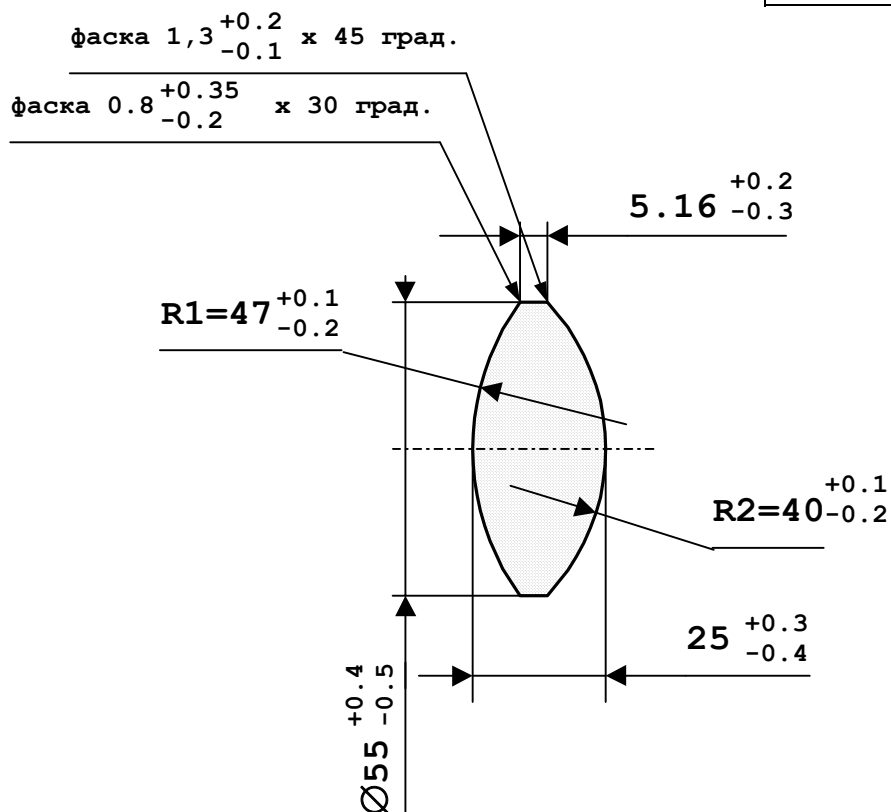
Пример оформления рабочего чертежа сферической линзы
